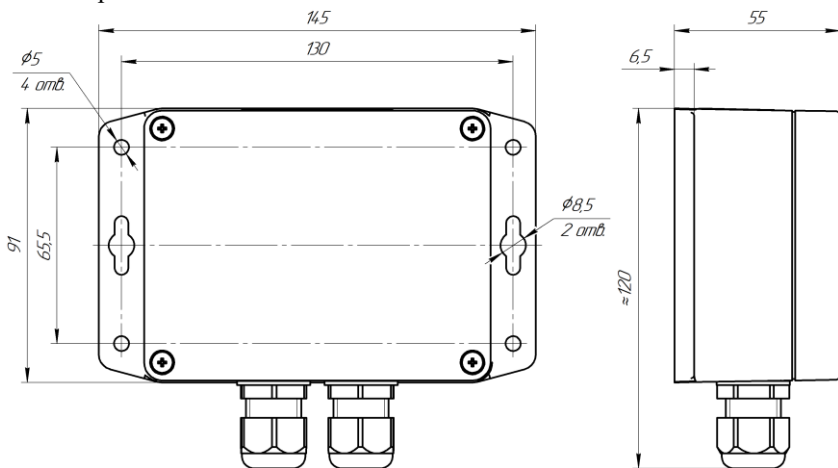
Габаритные размеры и отверстия для монтажа датчика GL-RCM.
